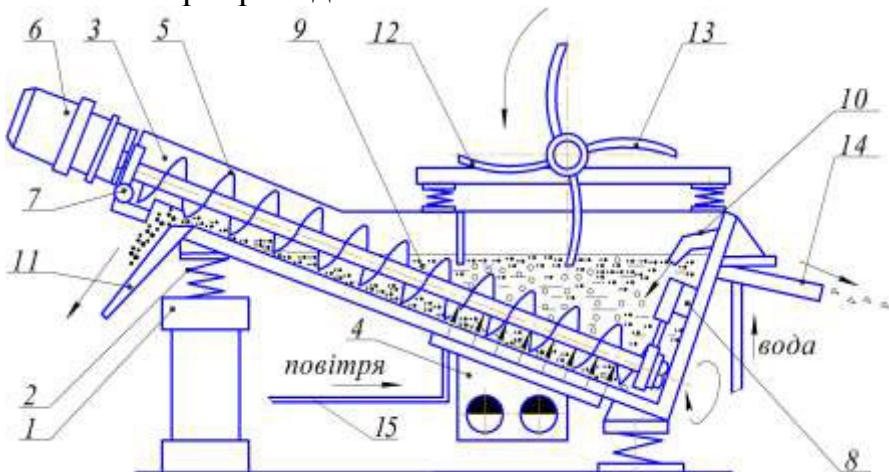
Вібраційний класифікатор з лопатковими захватами для вилученням корисної копалини
